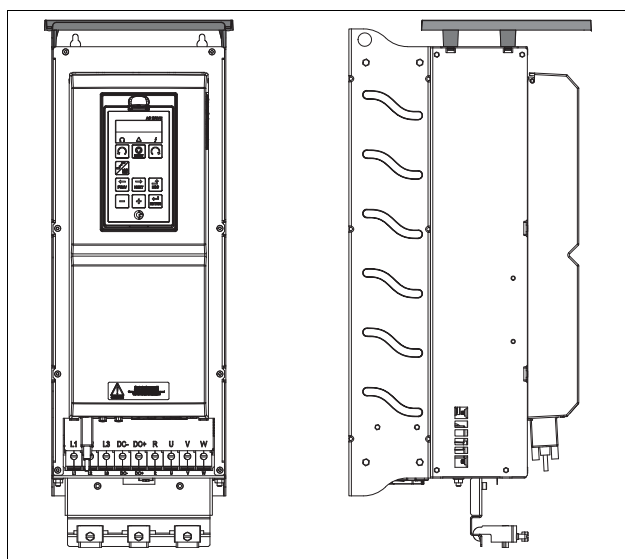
Дополнительная верхняя крышка, установленная на корпусе типоразмера D2
